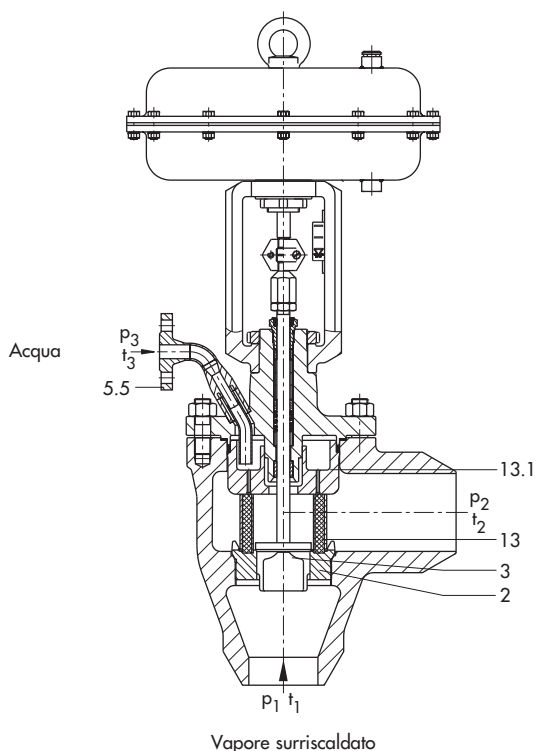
· Desurriscaldatore pneumatico Tipo 3286-1 con attacchi a saldare e attuatore Tipo 3271
